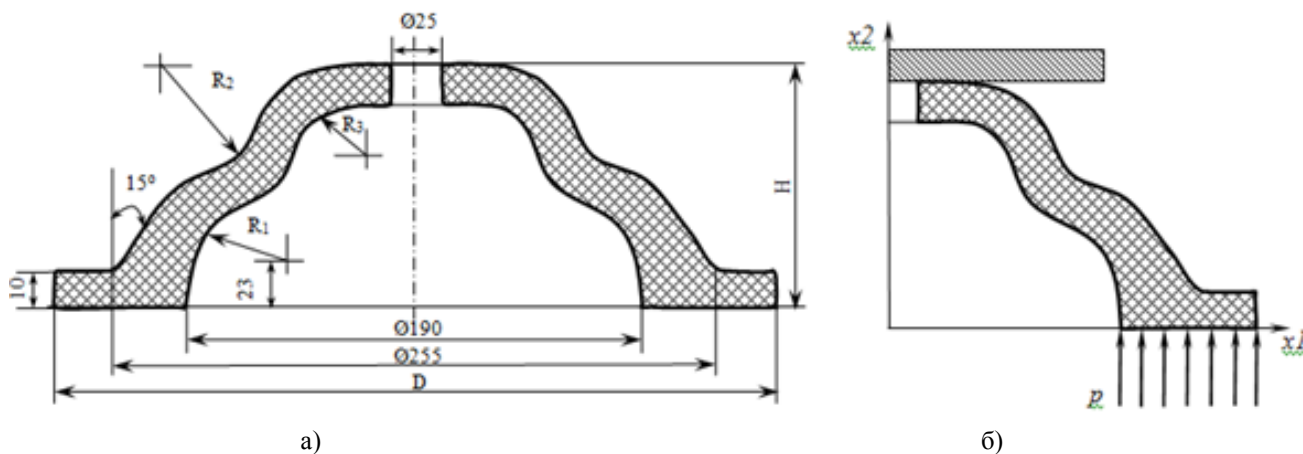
Виброизолятор ВН-200: а) поперечное сечение, б) расчетная схема
